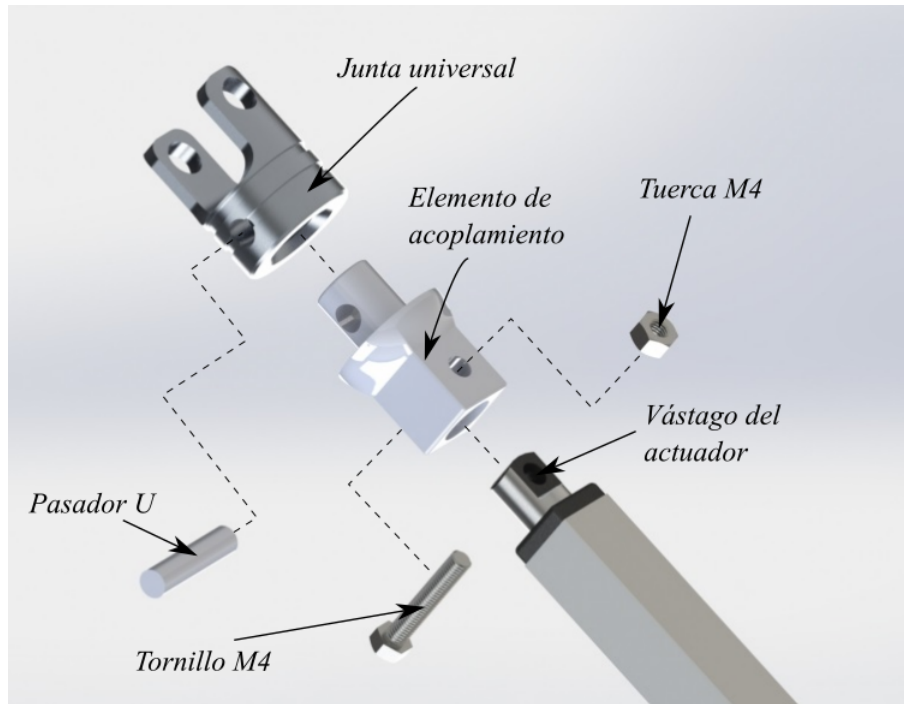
Dibujo explosionado de los elementos en la parte superior de las extremidades.
